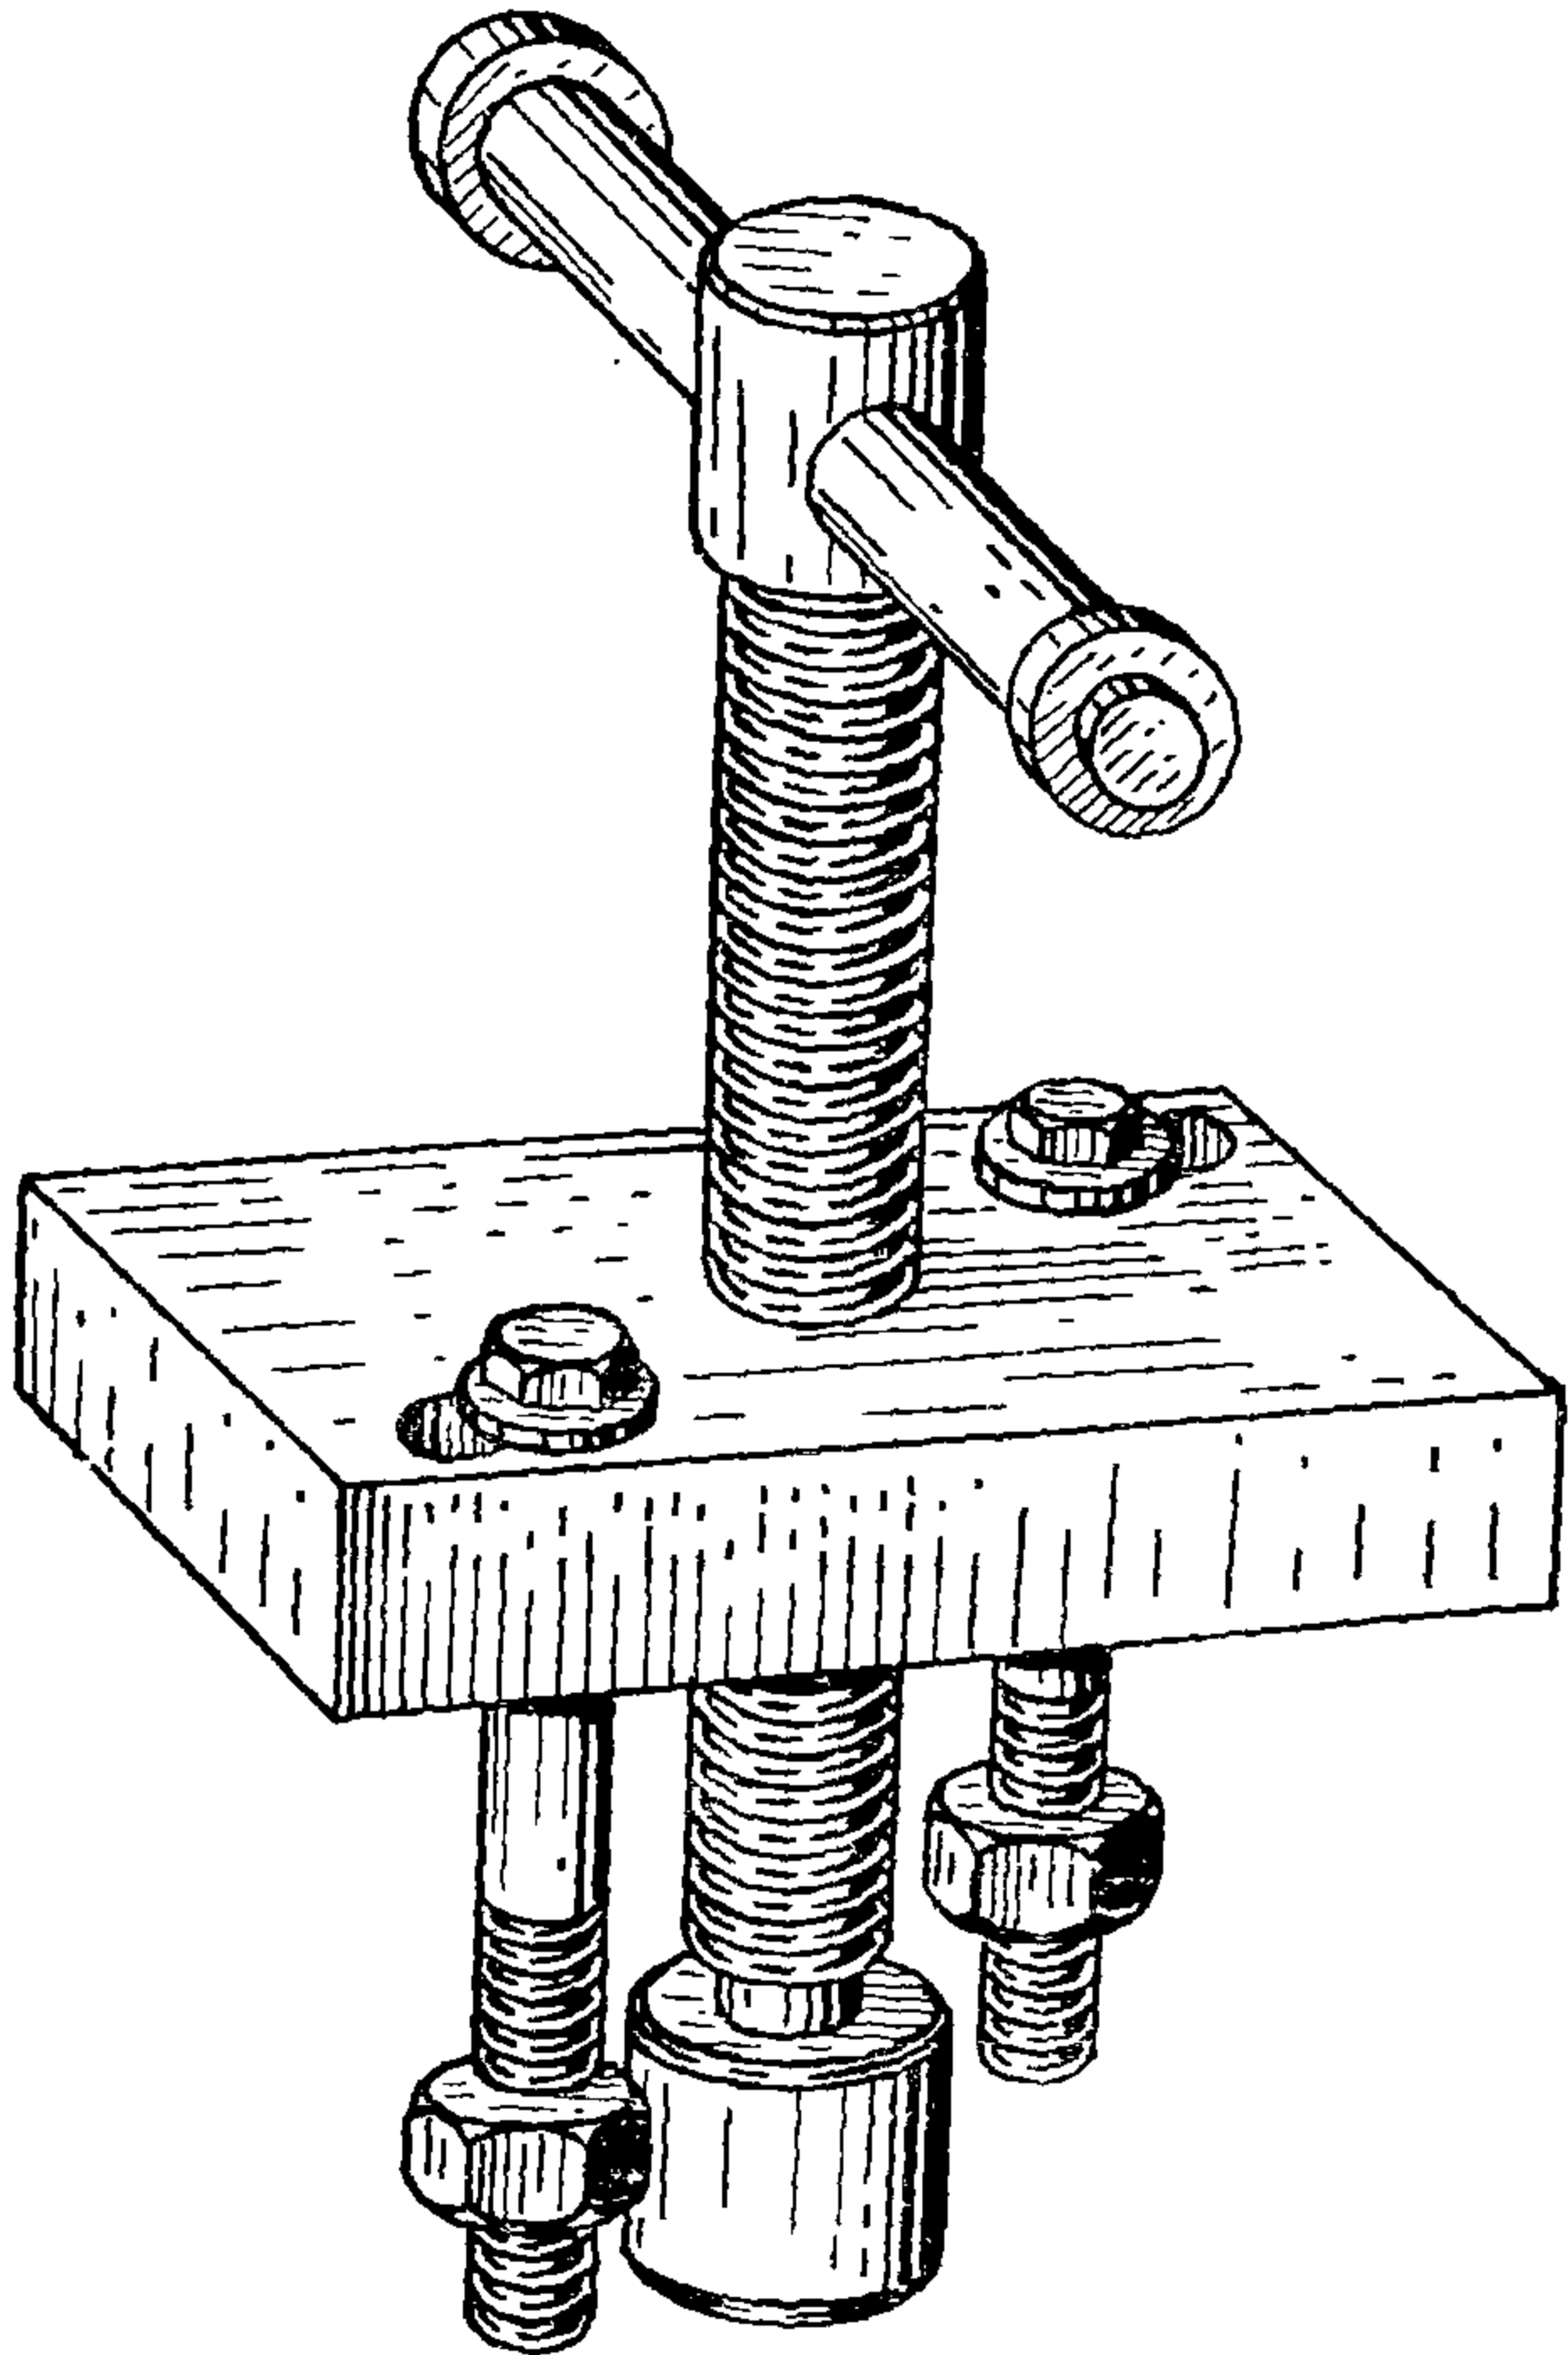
Приспособление для снятия маховика и корпуса заднего подшипника
